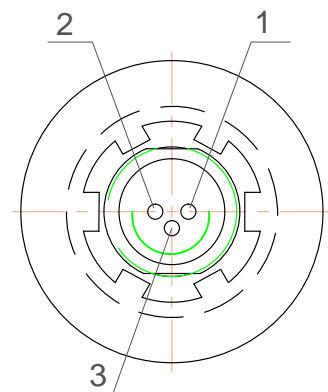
Схема расположения контактов выходного соединителя.
